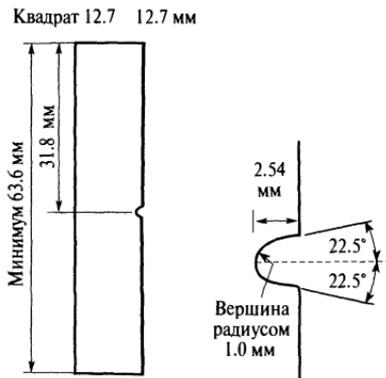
Стандартный полимерный образец для испытания по Изоду
